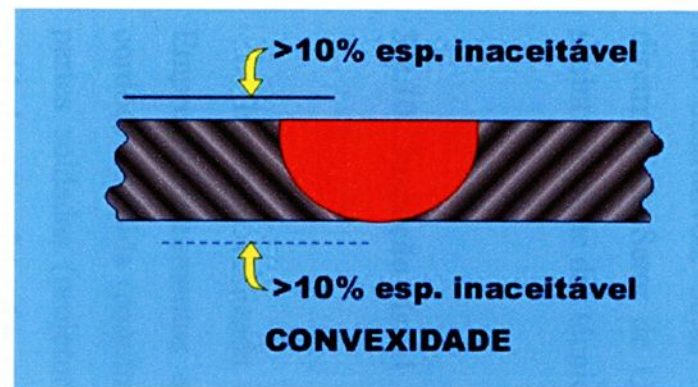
Condições de aprovação e rejeição dos cordões de solda
